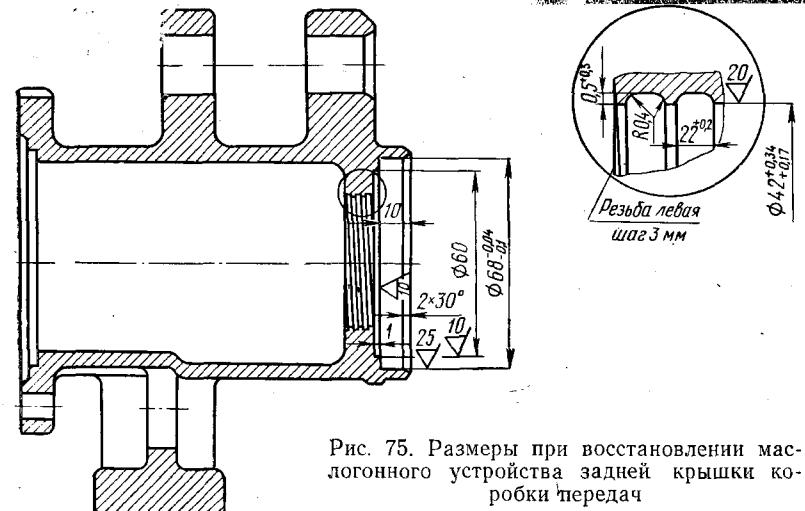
Размеры при восстановлении маслогонного устройства задней крышки коробки передач
